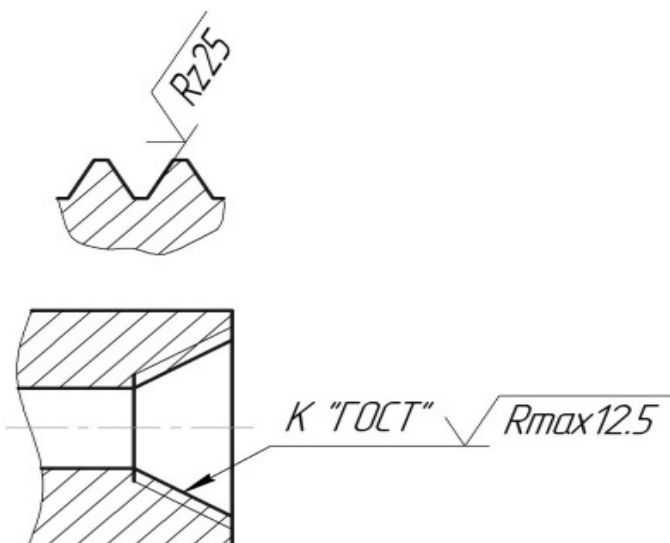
Пример обозначения шероховатости внутренней конической резьбы
